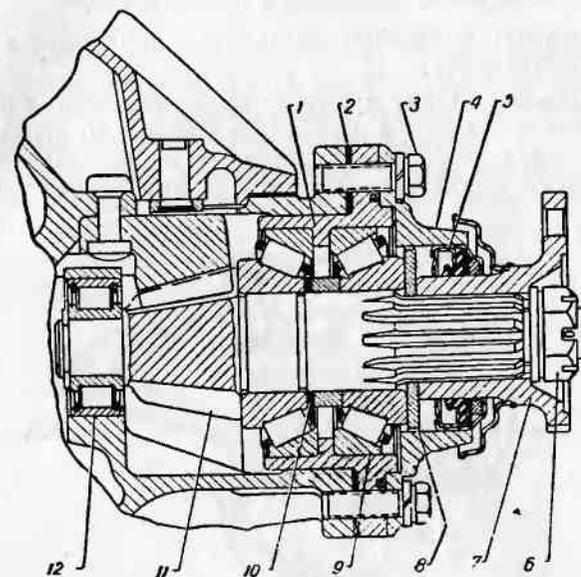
Ведущая шестерня главной передачи в сборе с подшипниками:
